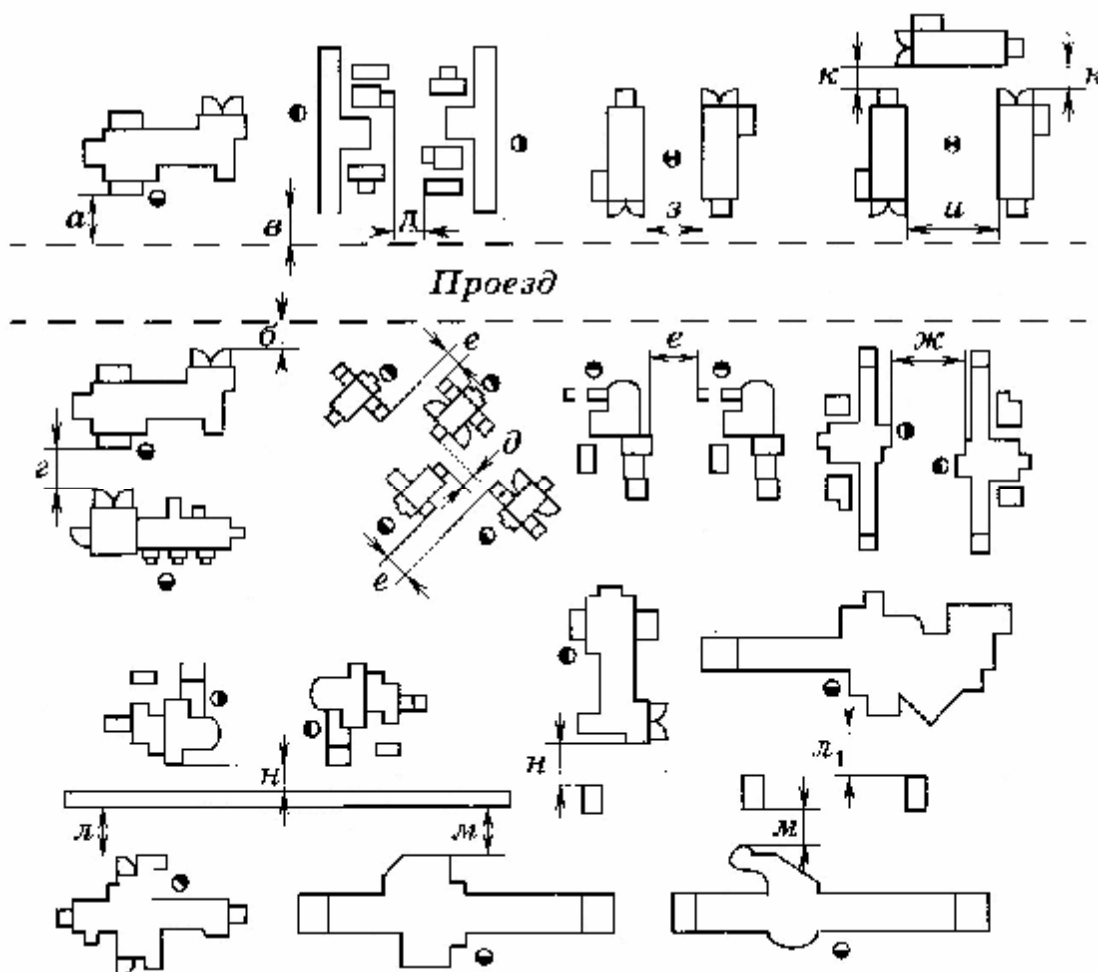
Варианты размещения станков относительно проездов, друг друга, стен и колонн здания
